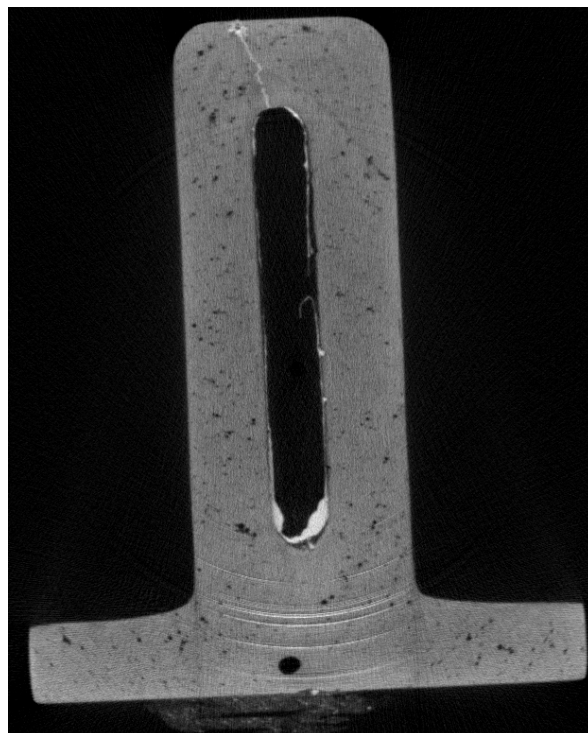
Sección de una pieza de cerámica con restos de fundición de aluminio. Se observa porosidad y una grieta rellena de fundición de aluminio.
